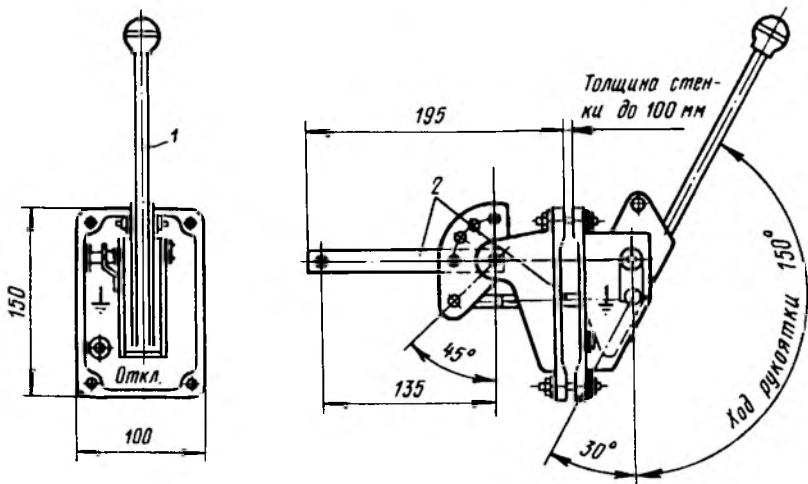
Схема ручного рычажного привода ПР-10 для управления разъединителями:
